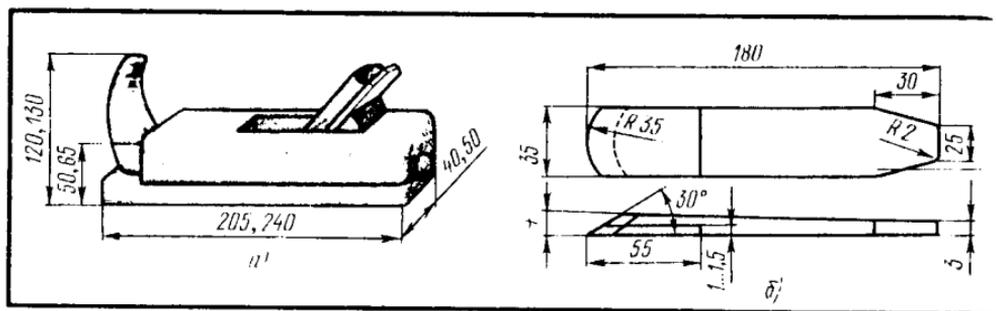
Шерхебель: а — общий вид, б — шерхебельный нож
